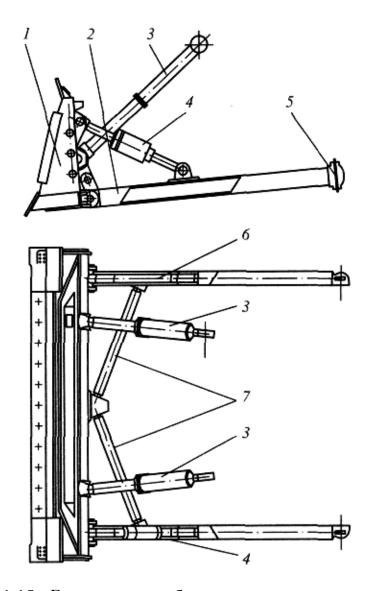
Бульдозерное оборудование с прямым отвалом: 1 - бульдозерный отвал; 2 - толкающий брус; 3 - гидроцилиндры подъема/опускания отвала; 4 - гидравлический подкос; 5 шарнир крепления толкающего бруса к раме гусеничной тележки (упряжной шарнир); 6 - винтовой подкос; 7 - горизонтальные раскосы.
